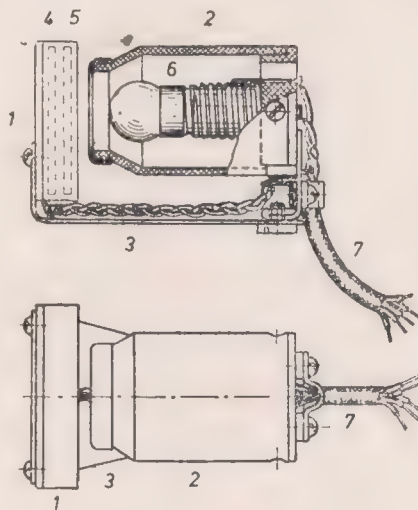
Geber. 1 Gehäuse des Fotoelementes, 2 Lampengehäuse, 3 Blattfeder, 4 Differential-Fotoelement, 5 Lichtfilter, 6 Glühlampe, 7 Anschlußkabel
